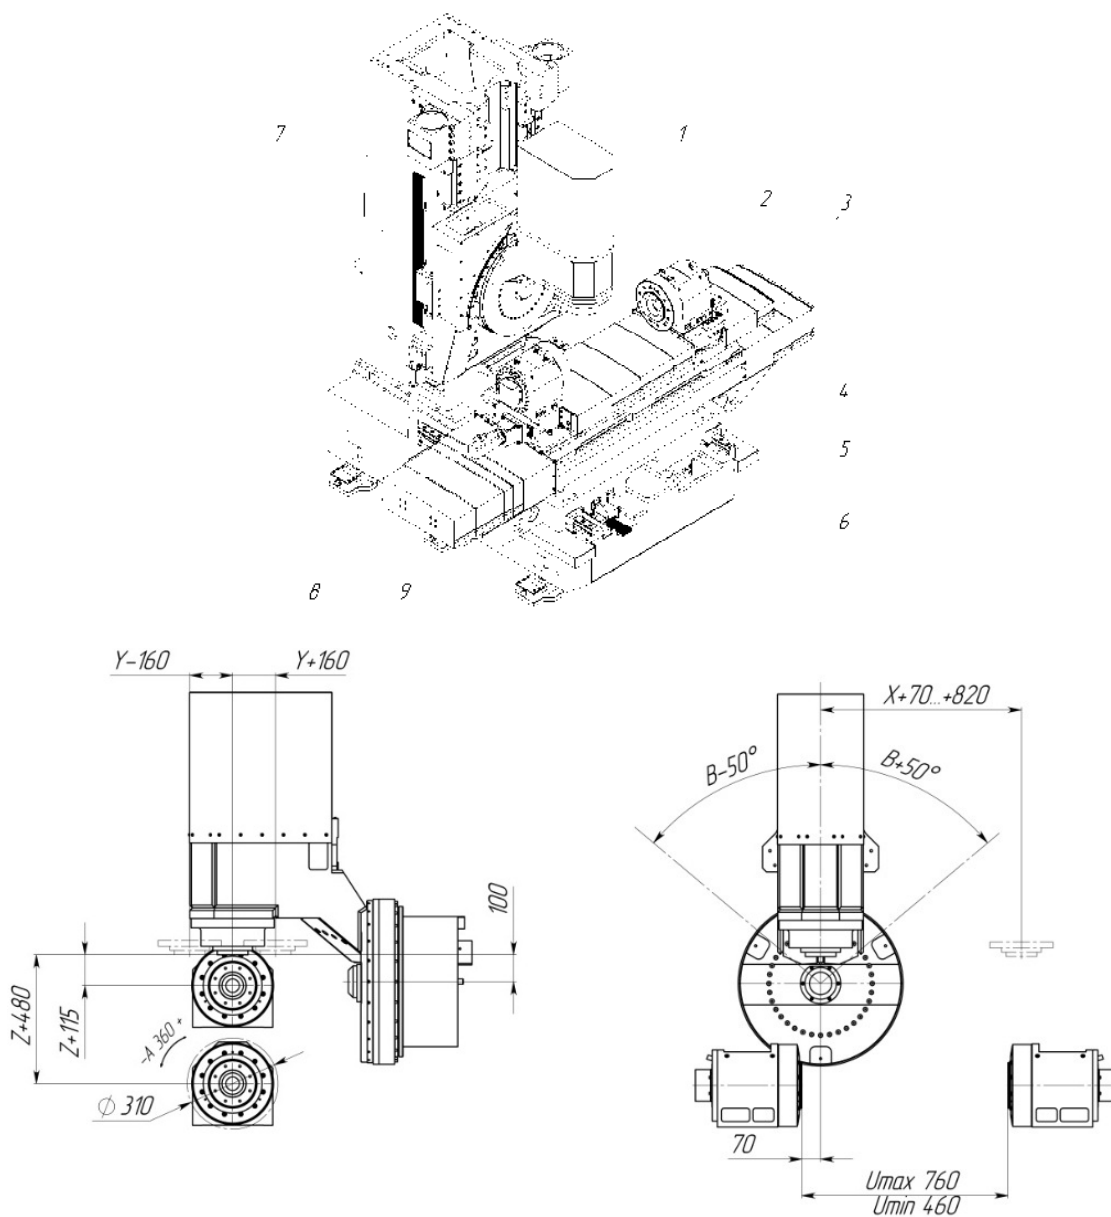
Схема базового верстата (до модернізації): 1-поворотна силова голова з фрезерним шпинделем, 2- поворотні головки, 3- телескопічні захисти, 4- плита, 5- полозки, 6- станина, 7- стійка, 8- гідроопора, 9- башмаки
